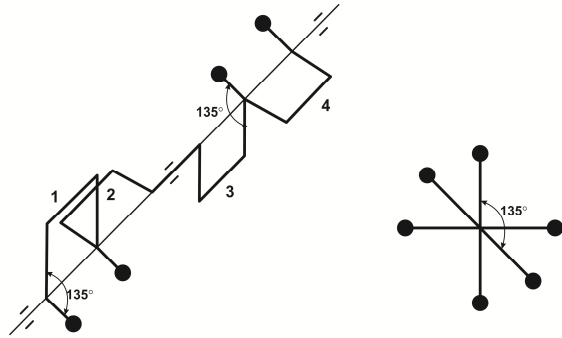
Схема коленчатого вала базового двигателя 4Ч 7,6×6,6
